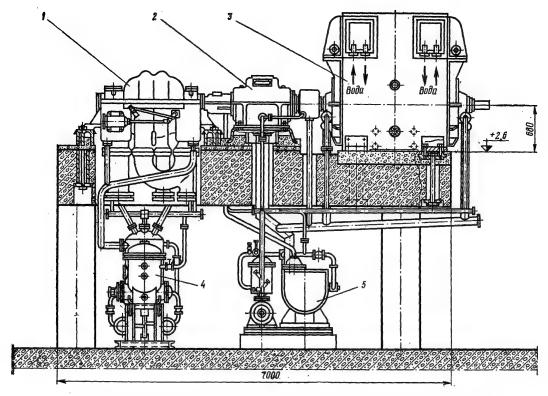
Пропановый центробежный холодильный агрегат АТКП-435-1600: 1 — компрессор; 2 — мультипликатор; 3 — электродвигатель; 4 — агрегат системы смазки компрессора; 5 — агрегат системы смазки привода.
